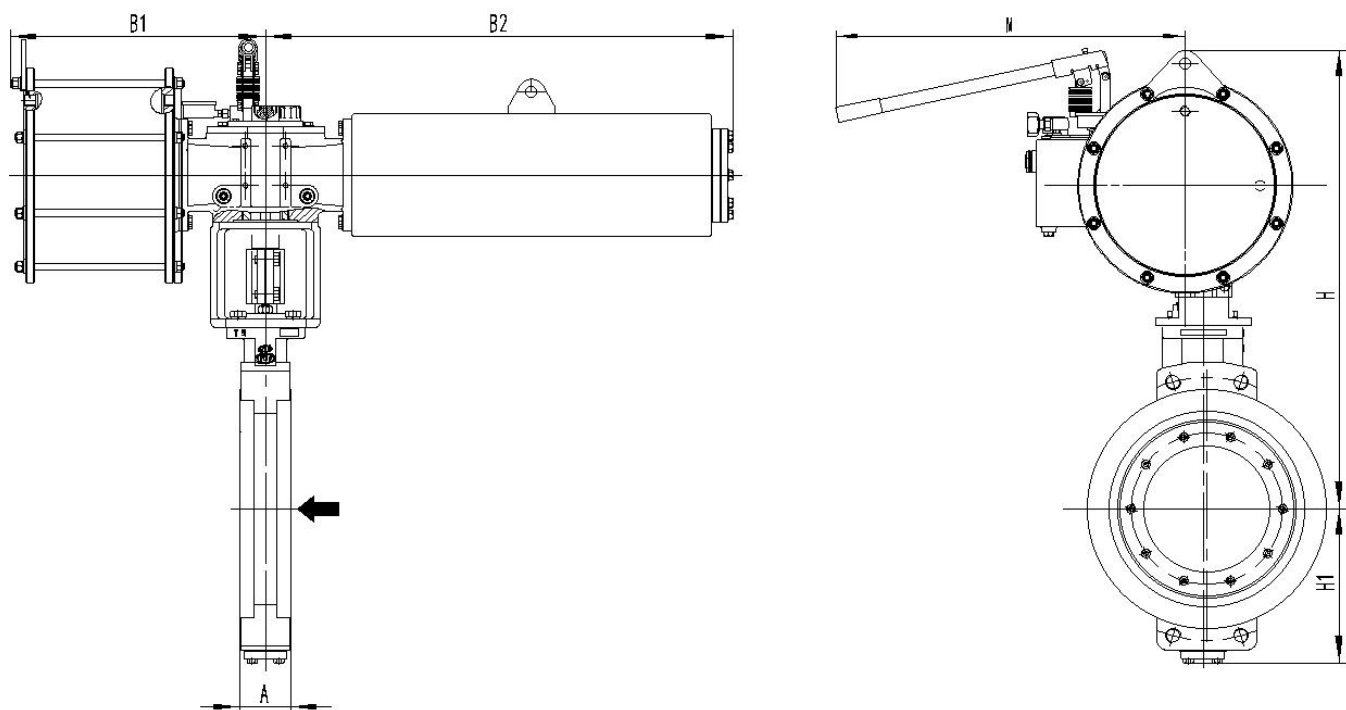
配 AW45SR43~AW85SR56 带液压手轮外形尺寸图 (FC)
